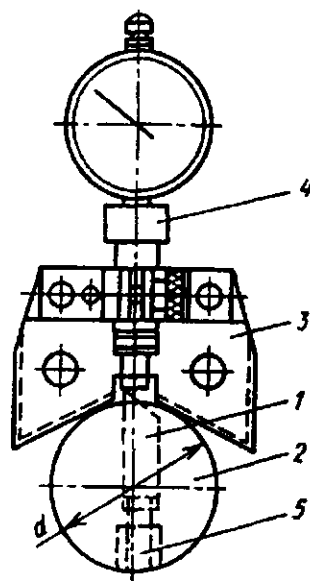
Магнитный прибор с призмой с выключением магнитов для установки и настройки резцов на размер: 1 — резец; 2 — борштанга; 3 — магнитный прибор с выключением магнита; 4 — индикатор прибора; 5 — упорно-регулирующий винт
